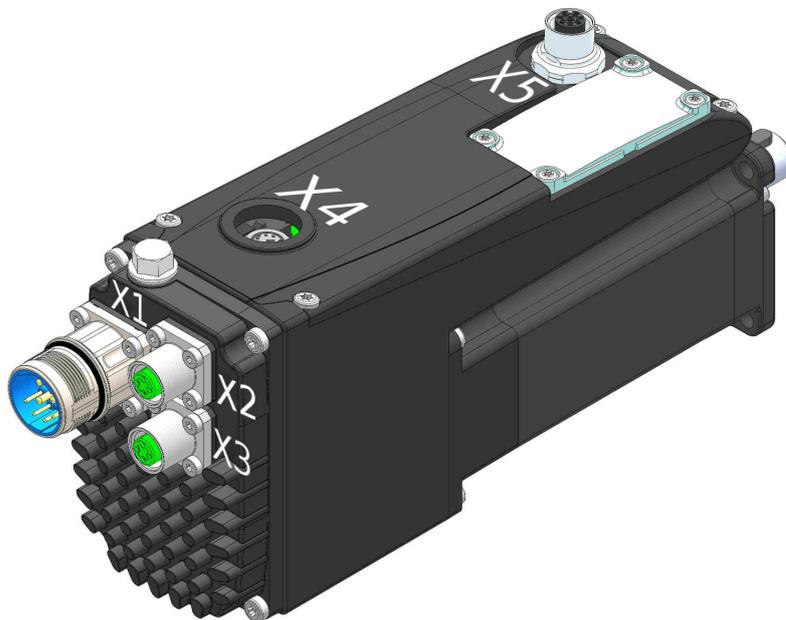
Disposizione dei connettori: vista posteriore flangia 60mm.
